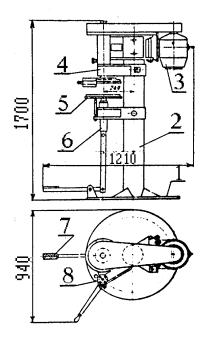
Неавтоматическая закаточная машина Р3-1: 1-плита; 2 – стойка; 3 – привод; 4 – закаточная головка; 5 – нижний патрон; 6 – прижимное устройство; 7 – педаль; 8 – роликодержатель
